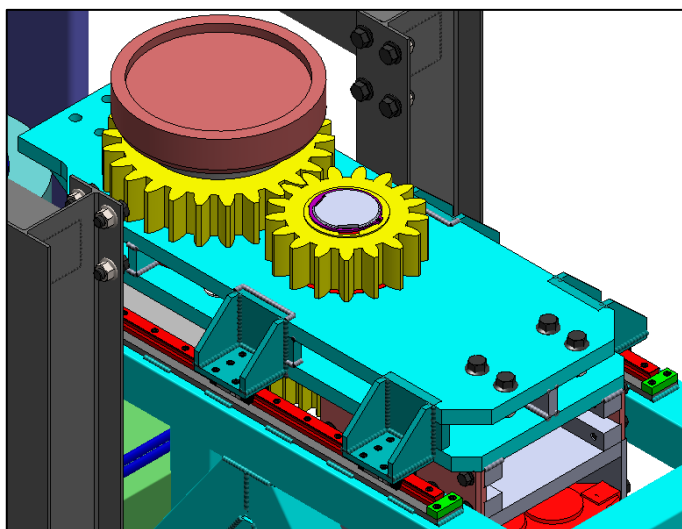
Representação esquemática em vista isométrica da montagem do sistema de transmissão instalado sobre a estrutura de guias lineares
